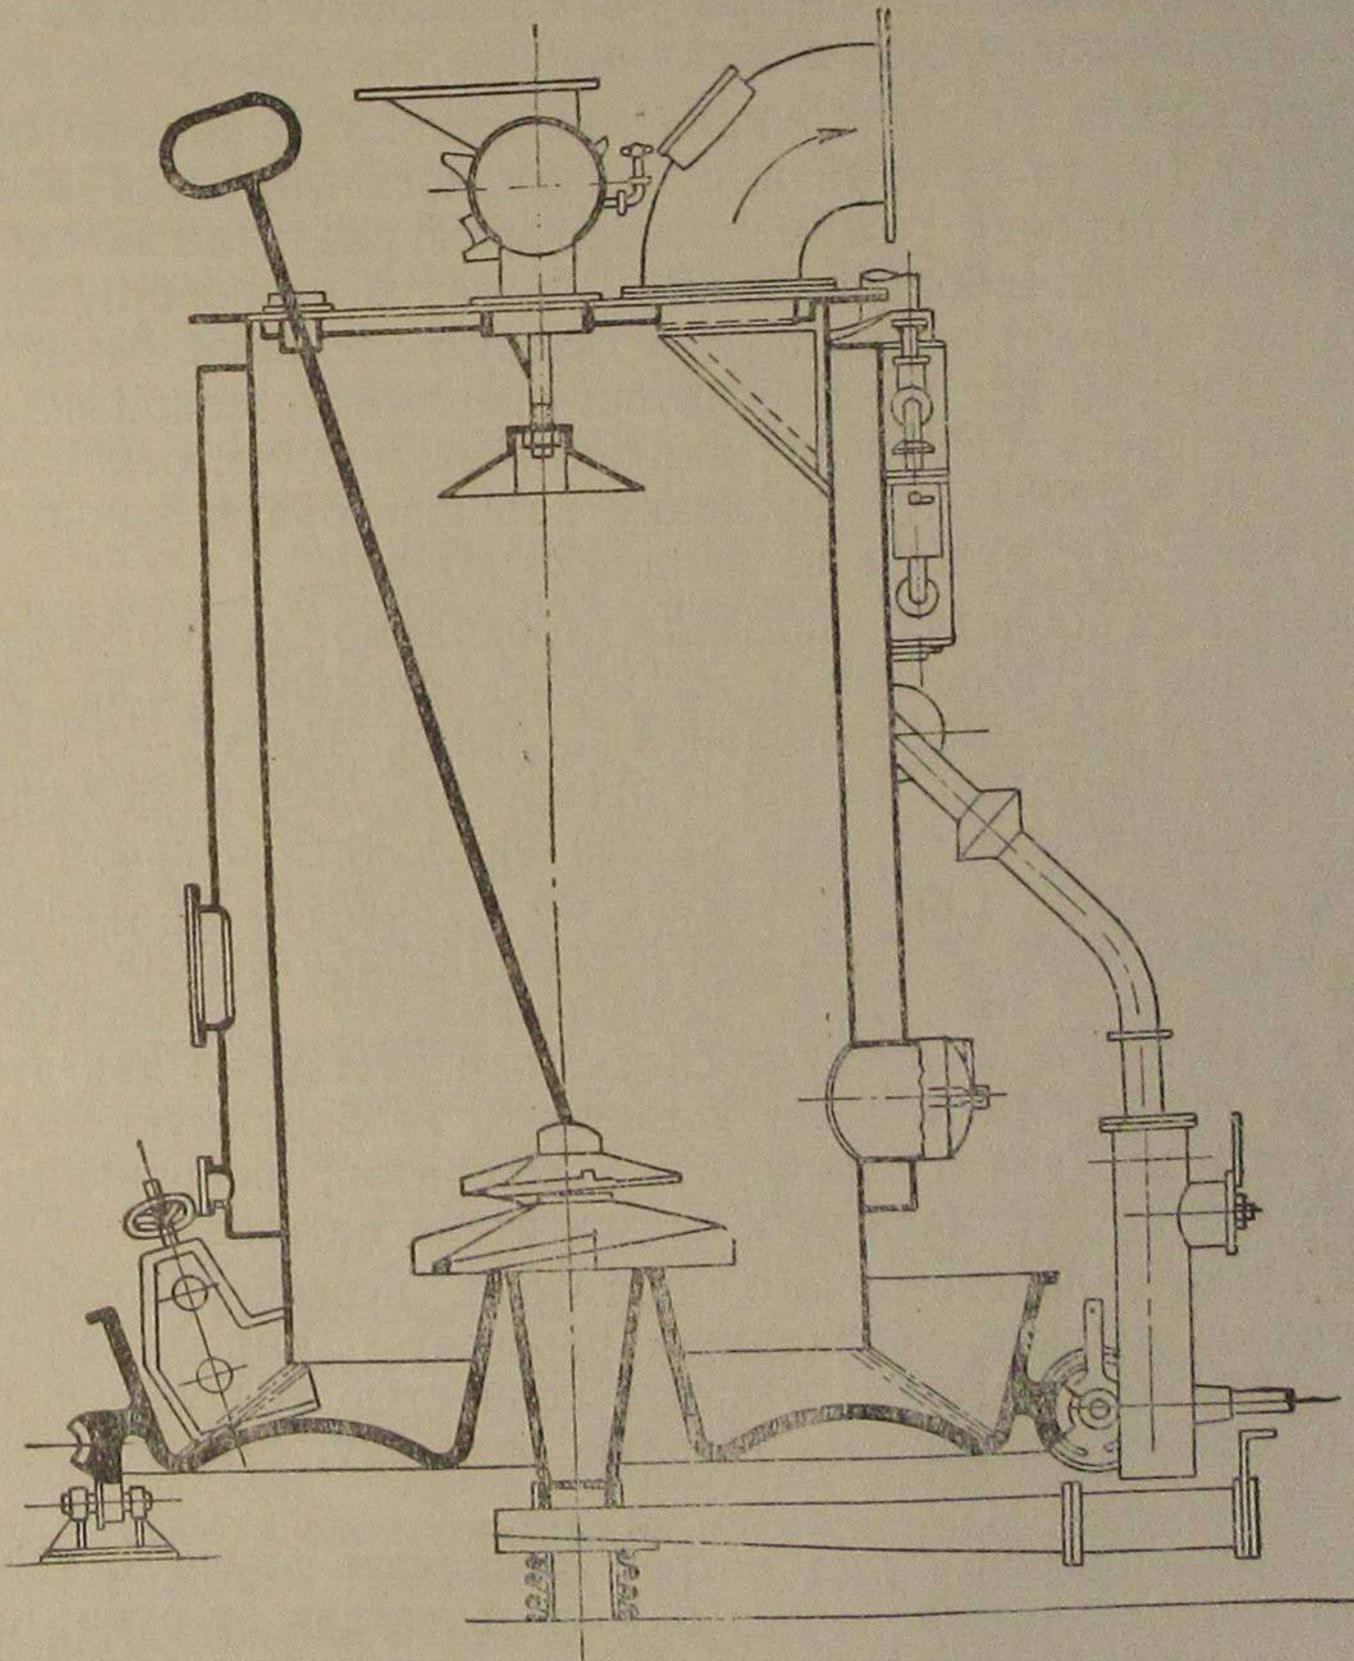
Установка шуровочной штанги на чепец колосниковой решетки механизированного газогенератора
